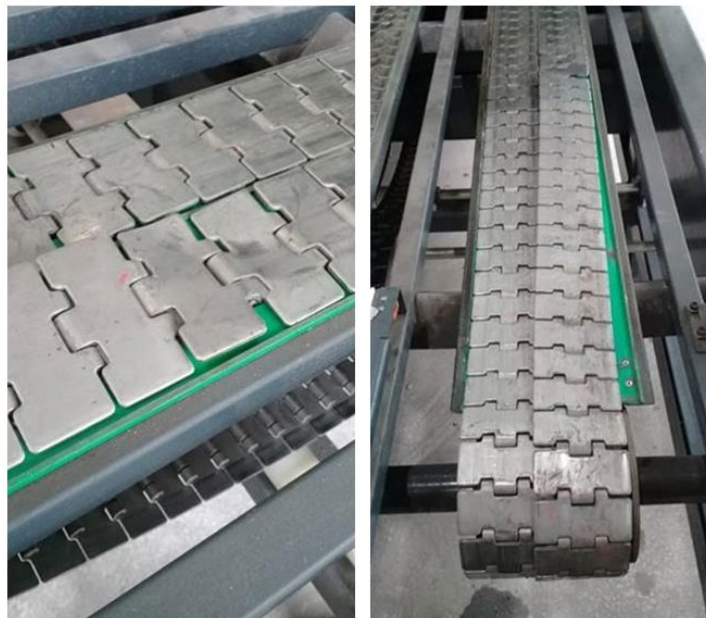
Eslabón deformado y descarrilamiento de cadena.
